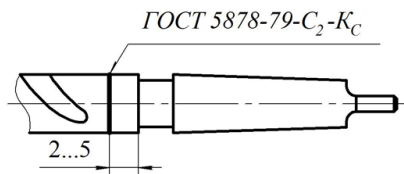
Расположение сварного шва на сверлах и пример его обозначения
